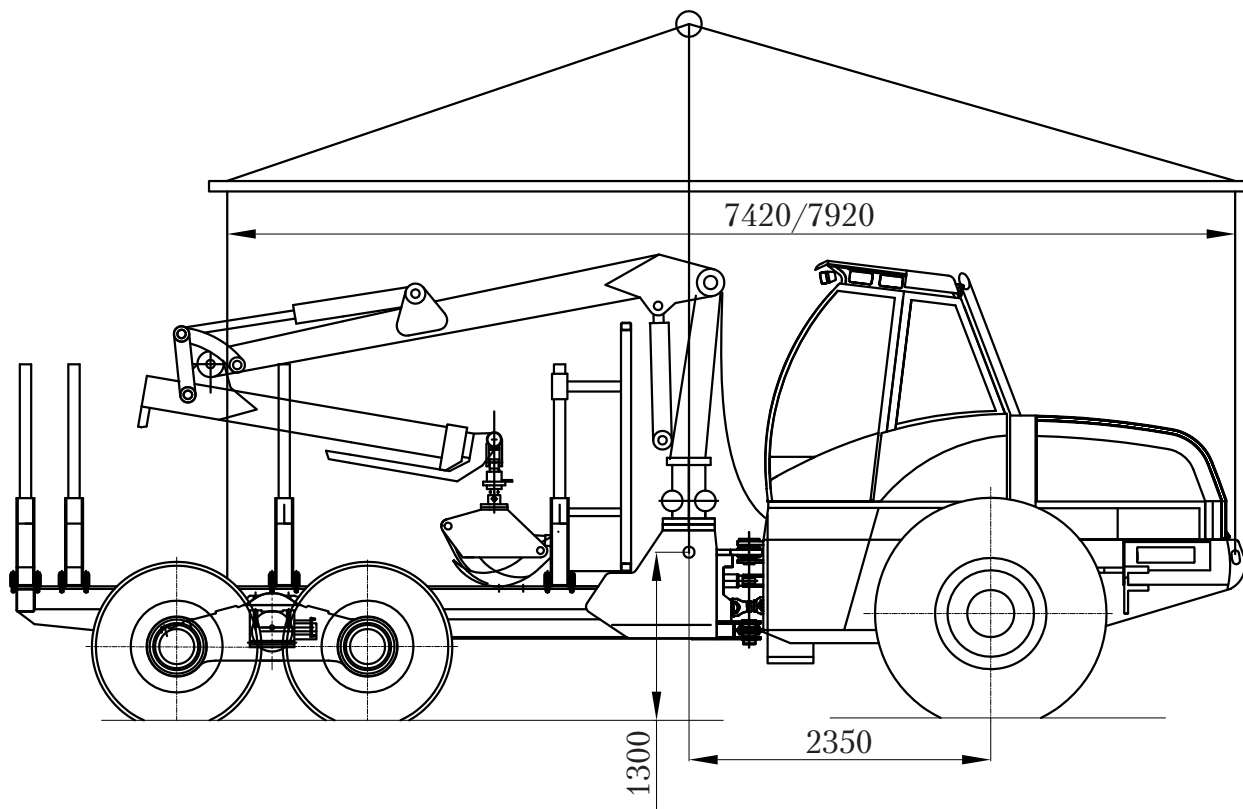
Схема строповки форвардера АМКОДОР 2661/2661-01
